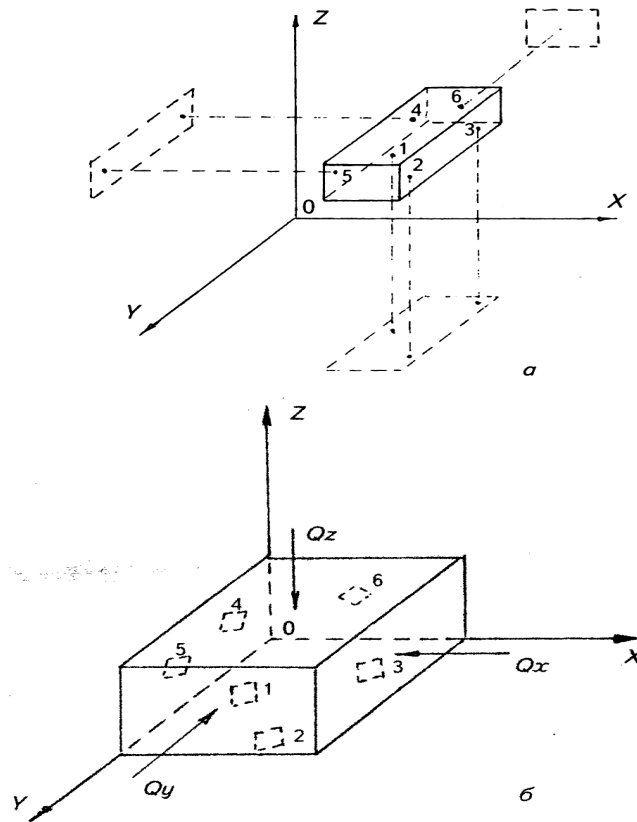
Схема базування призматичної заготовки: *а* - положення заготовки у системі координат; *б* – положення заготовки у технологічному пристрої
